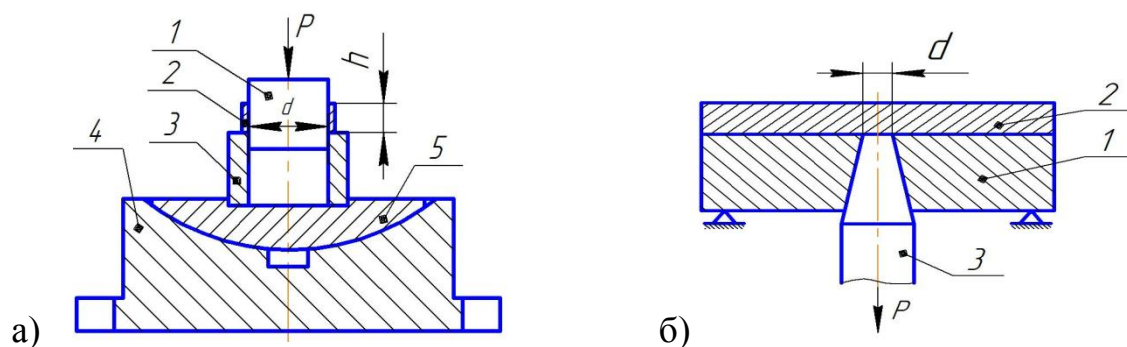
Схеми випробовування покриттів на зріз (а):
